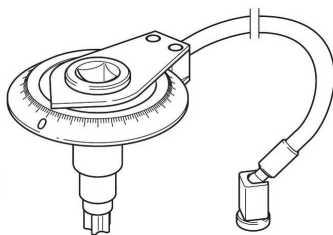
Приспособление для регулировки теплового зазора двигателей Deutz
